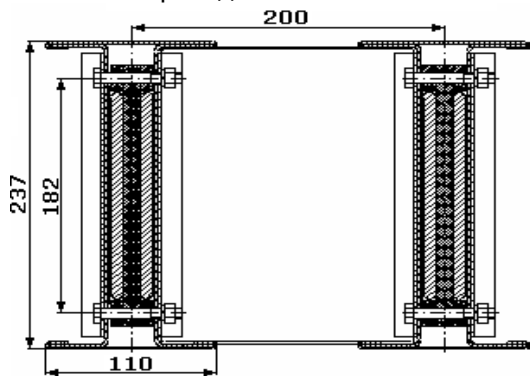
Поперечное сечение шинопровода на ток 3200А.
